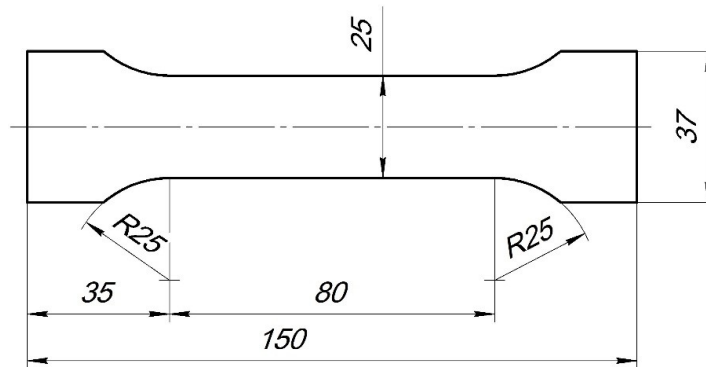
Геометрические размеры образца для испытаний на статическое растяжение
